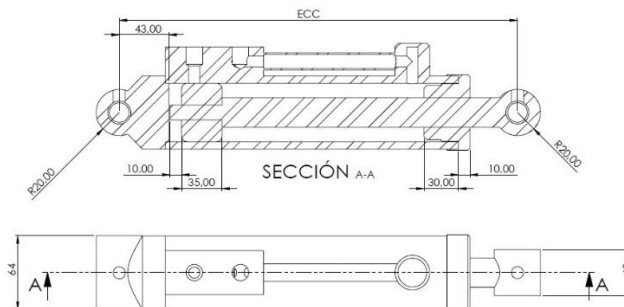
Dimensiones constructivas cilindro 2" ECA
